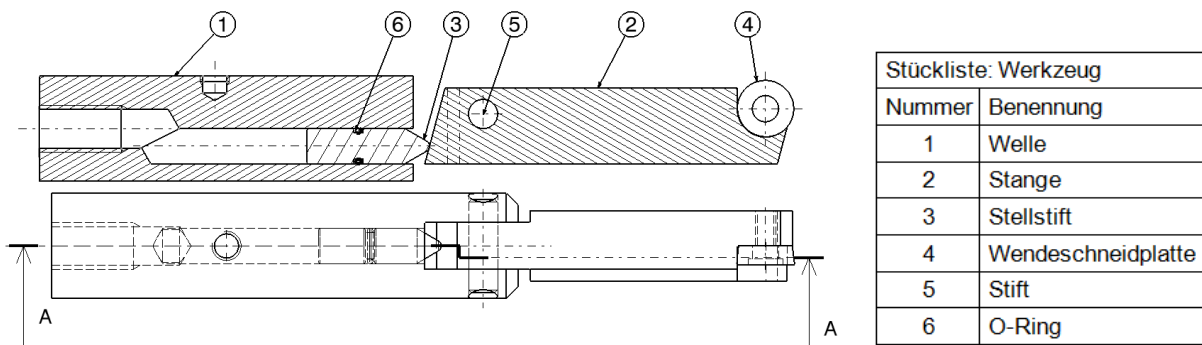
Werkzeug mit hydraulischer Auslenkung und Schneidplatte
